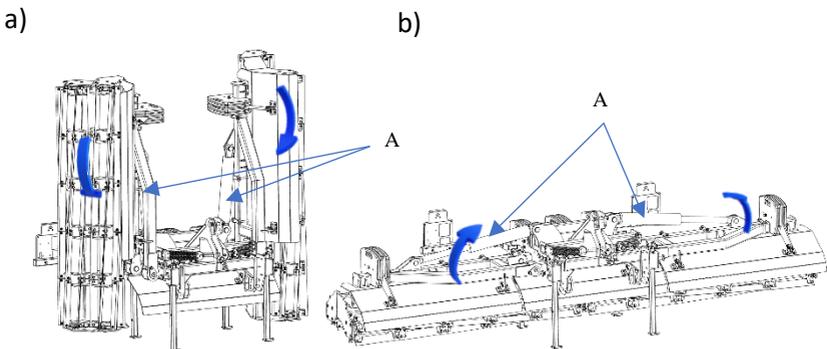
Manipulation der Seitenteile der Maschine; (a) eingeklappte Maschine, (b) ausgeklappte Maschine.
